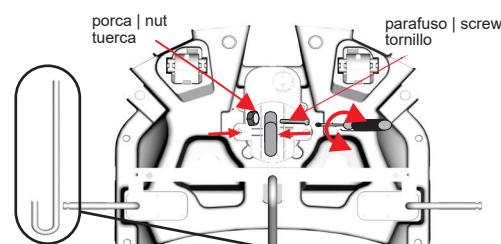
Eixo de Direção | Steering shaft | Eje de Dirección
